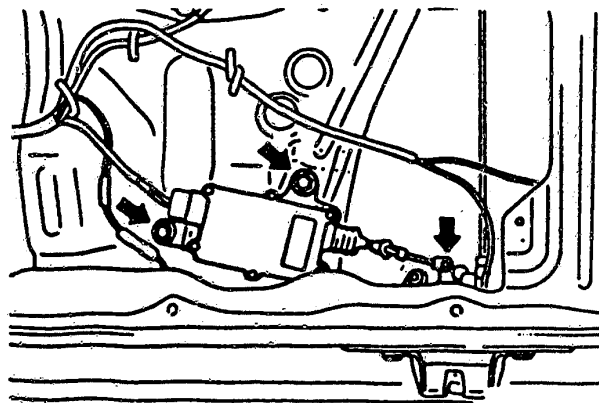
Der Elektromotor für die Heckklappen-Verriegelung ist mit zwei Schrauben an der Heckklappe befestigt.
